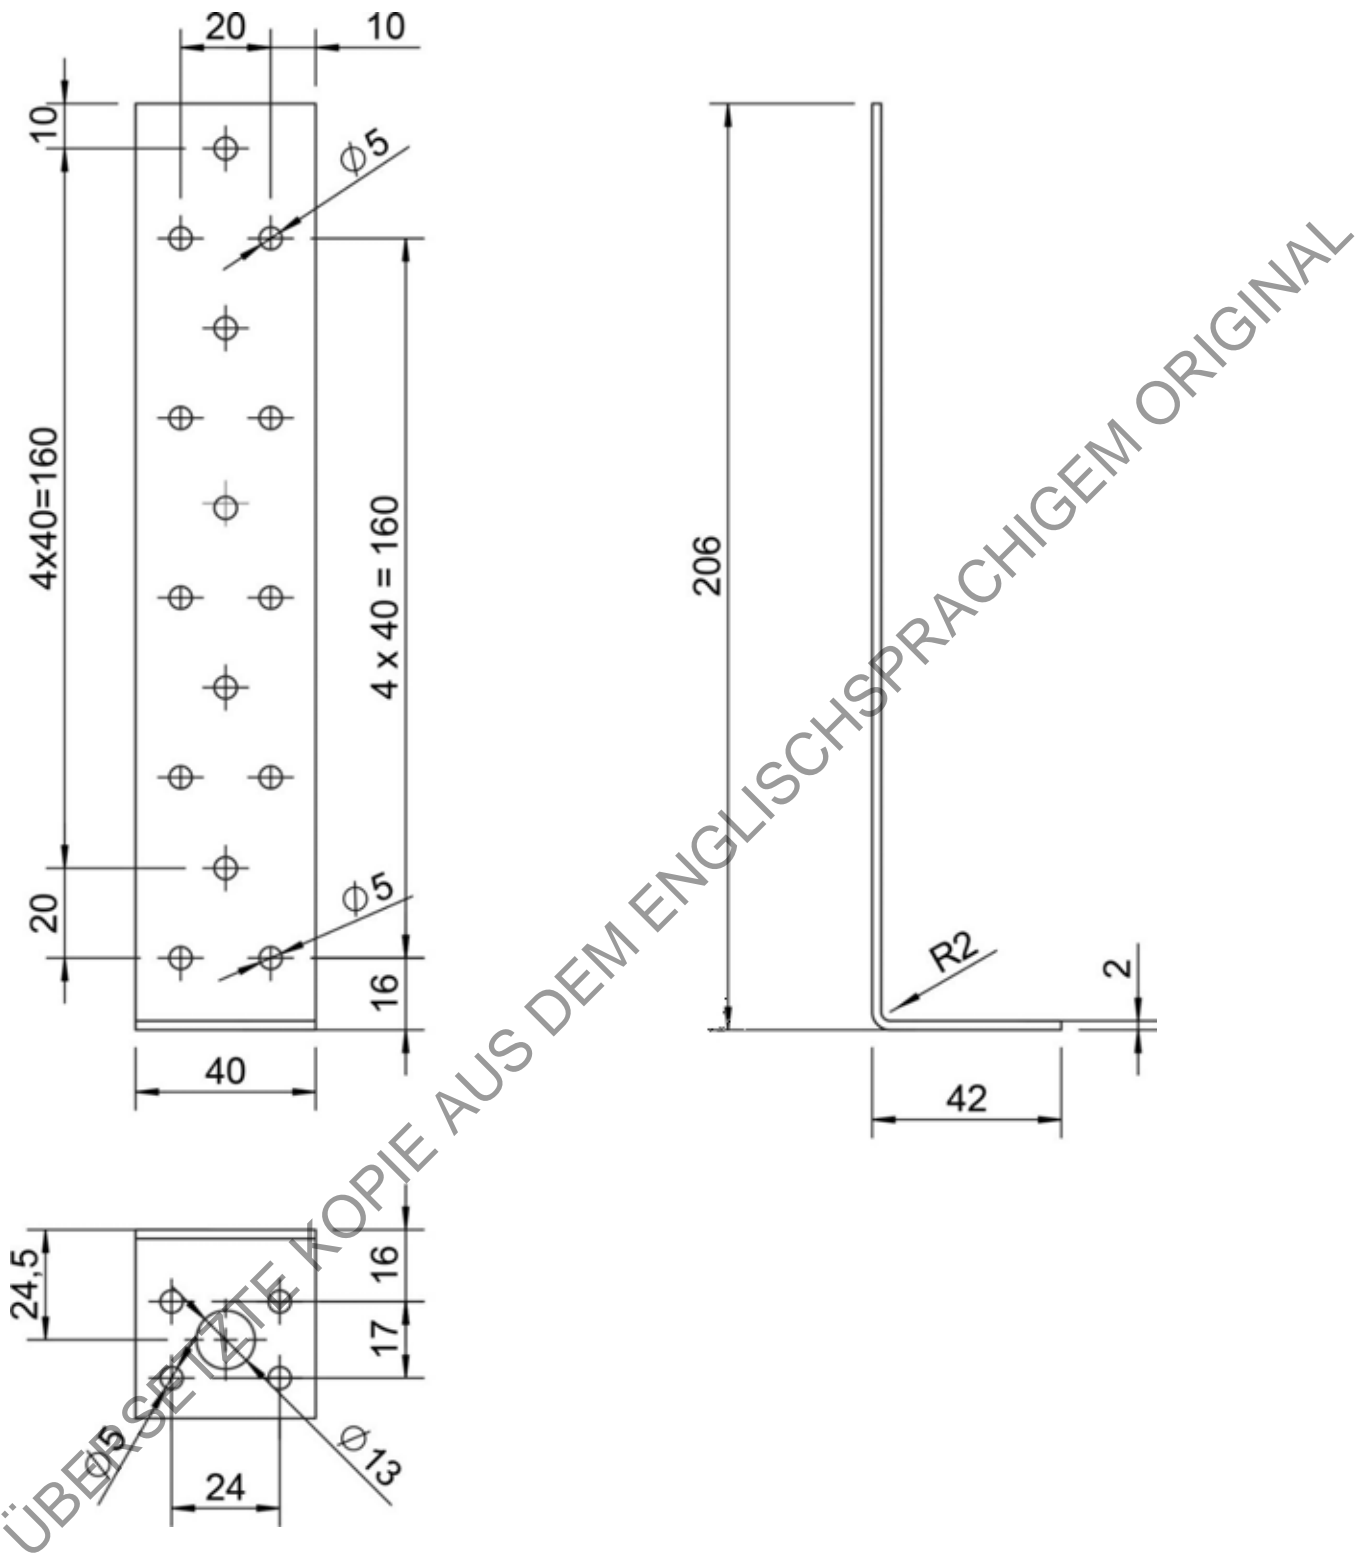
Abmessungen eines Beton-Flachstahllankers 200x40x40x2,0
